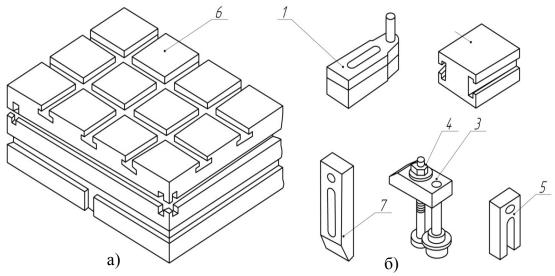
Универсально-сборное приспособление для обработки параллельных пазов: а — общий вид; б — элементы приспособления
